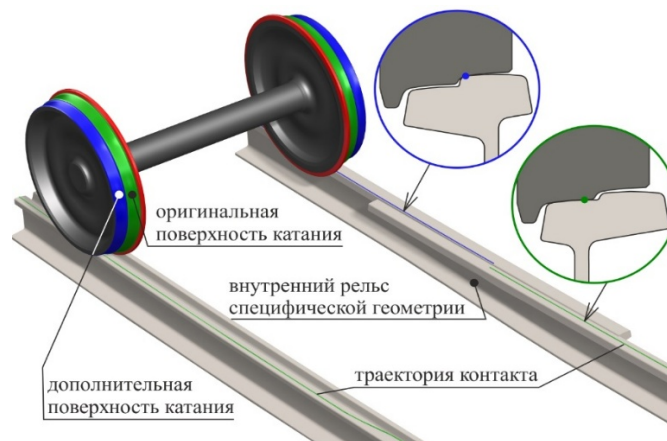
Схема предлагаемой конструкции колёсной пары с дополнительной поверхностью катания, расположенная на вьезде в кривой участок пути специфической конструкции
